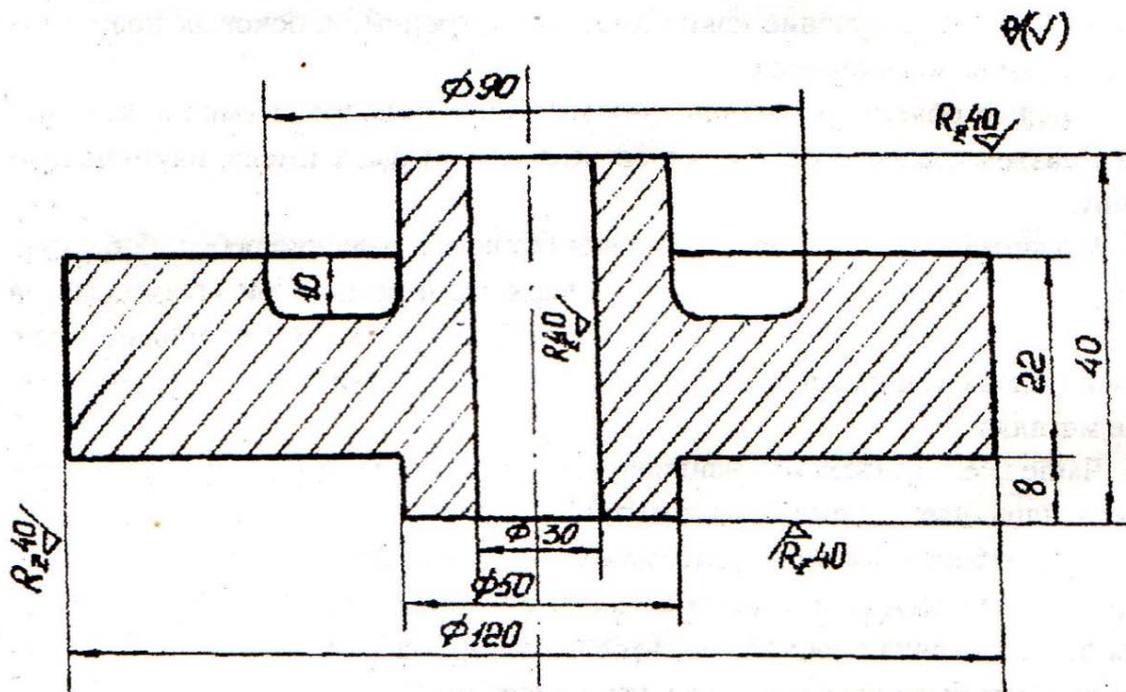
Чертеж детали. Масса детали 1,5 кг. Материал детали – сталь 20.
